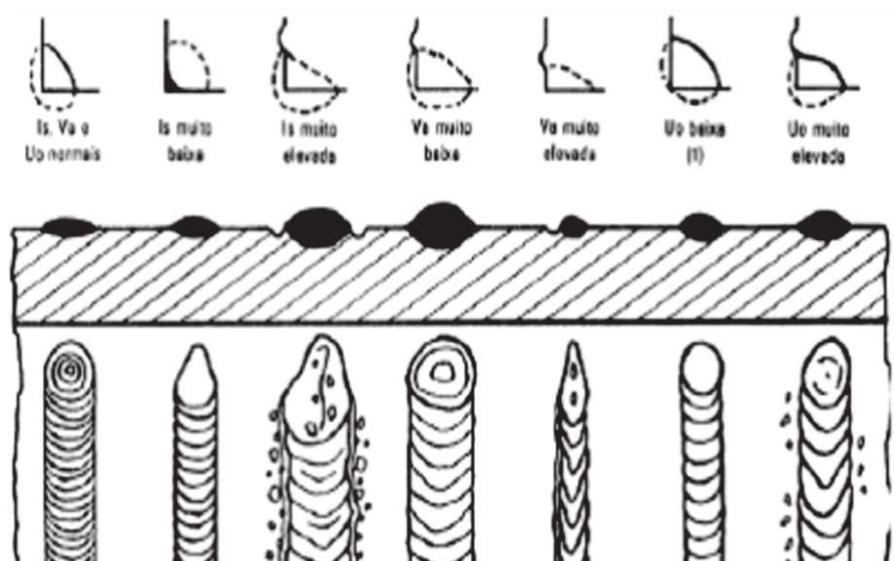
Influência dos parâmetros de soldadura no cordão.
